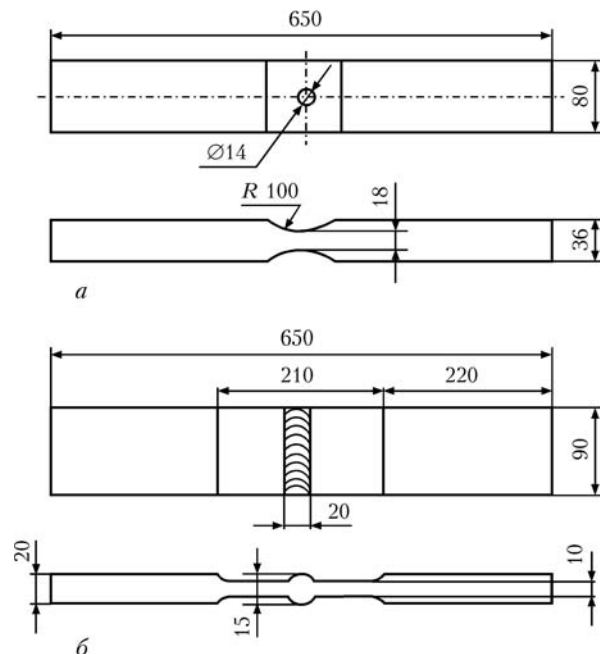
Схемы образцов для усталостных испытаний при одно- и поличастотном нагружении из основного металла с центральным отверстием (а) и со стыковым сварным соединением (б)
